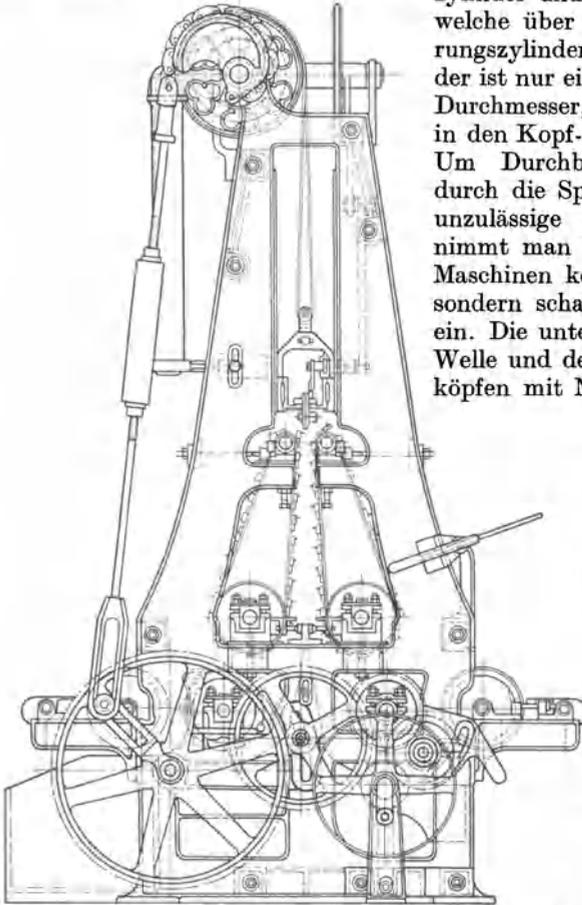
Skizze einer Bürsten-Doffer-Hechmaschine (Stephen Cotton & Co. Ltd., Belfast).
